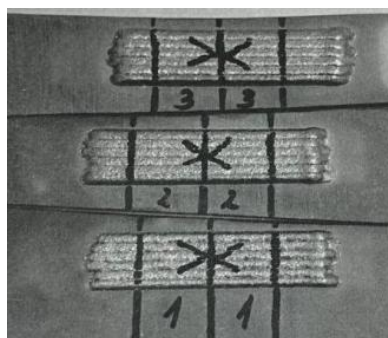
Внешний вид наплавленных образцов при мощности лазерного излучения:
